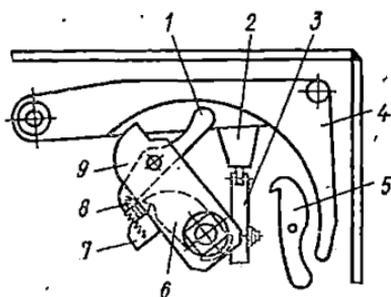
Регулировка включающего и удерживающего механизма привода ПП-67:
